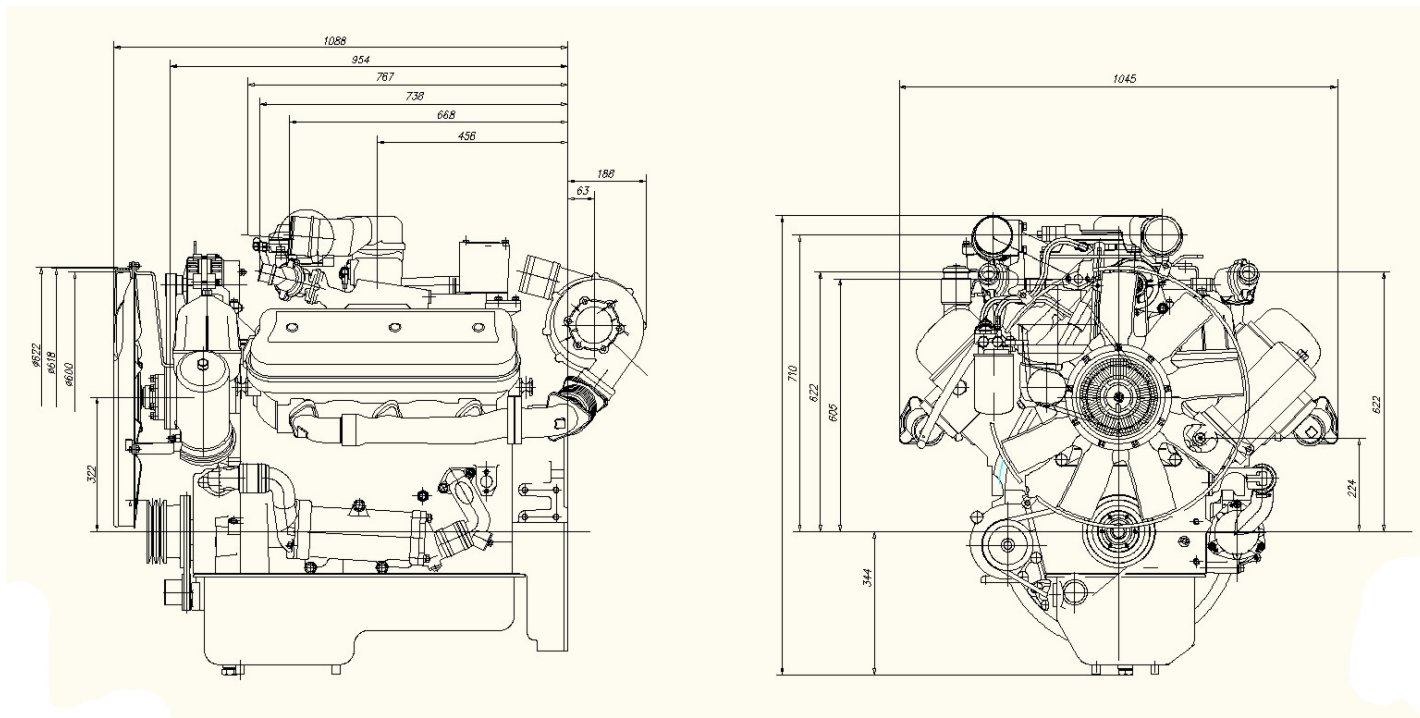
Габаритные размеры (в мм) двигателя ЯМЗ-6565
